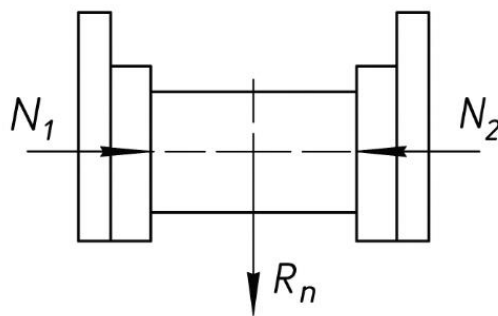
Реакції в точках контакту між заготовкою і губками захоплювача
